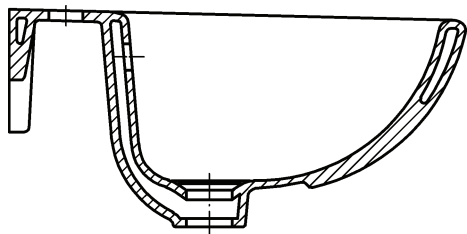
Wandhängendes Waschbecken mit Überlauf
